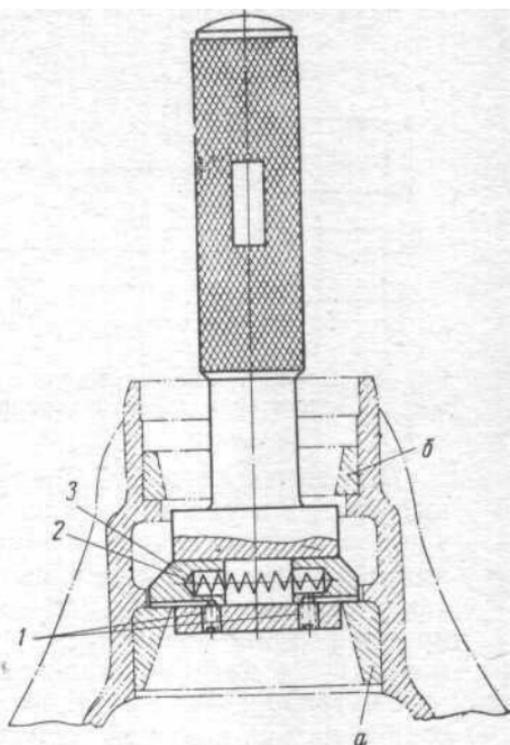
Оправка для выпрессовывания наружного кольца заднего подшипника вала ведущей шестерни главной передачи:
